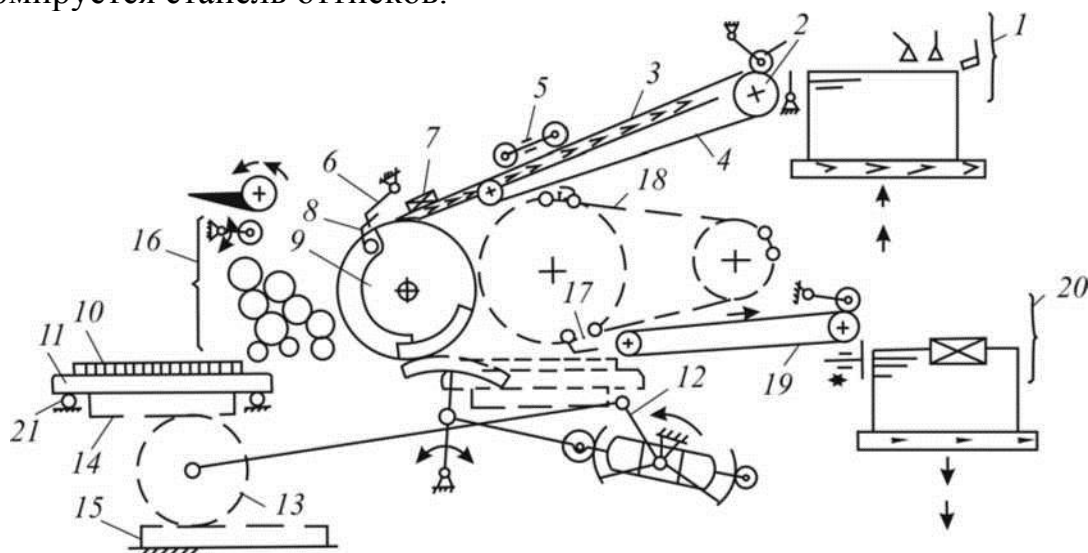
Принципиальная схема однооборотной плоскостаночной машины: 1 - листопитающее устройство; 2 - приемные ролики; 3 - наклонный стол; 4, 19 - тесемочные транспортеры; 5 - грузовые ролики; 6 - передние упоры; 7 - боковой упор; 8 - захваты печатного цилиндра; 9 - печатный цилиндр; 10 - форма; 11 - талер; 12 - кривошип; 13 - шестеренчатый скат; 14, 15 - зубчатые рейки; 16 - красочный аппарат; 17 - захваты листовыводного транспортера; 18 - цепной листовыводной транспортер; 20 - приемное устройство; 21 - роликовые подвижные опоры
